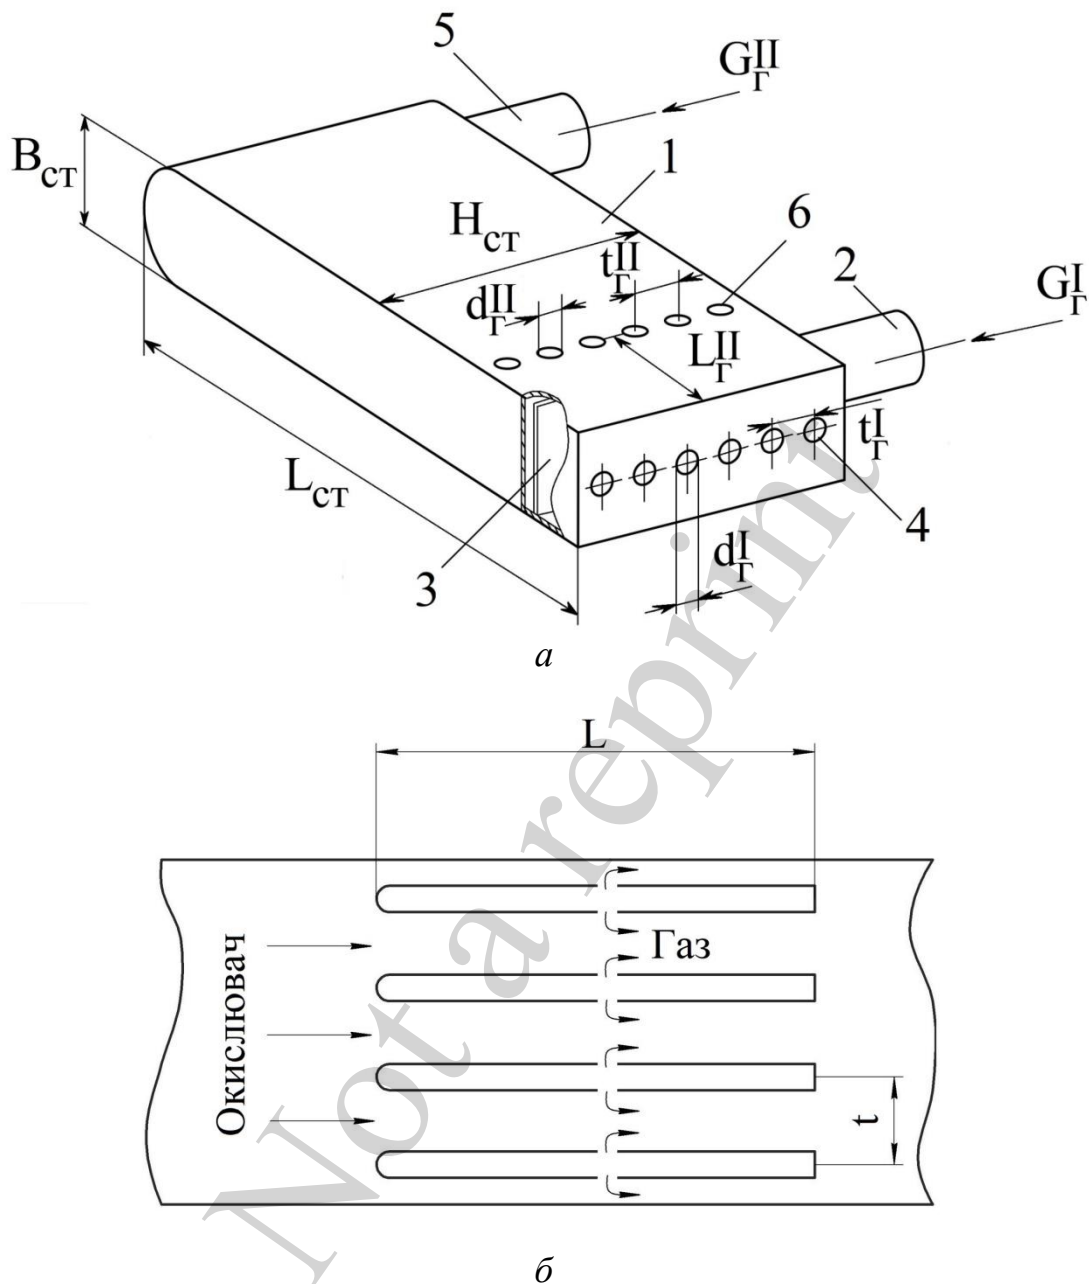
Пальниковий пристрій для спалювання газу: *a* – модульний стабілізатор для комбінованого спалювання газів; *б* – стабілізаторний мікрофакельний пальниковий пристрій; 1 – корпус; 2, 3, 4 – патрубок, камера і отвори подачі газу в зону рециркуляції (I схема); 5, 6 – патрубок і отвори подачі газу в обтічний повітряний потік (II схема)
